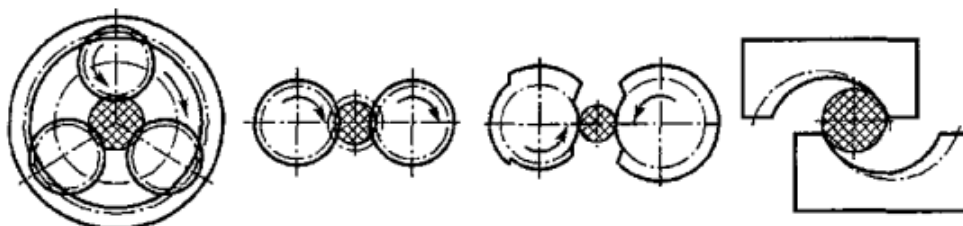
Обробка зубів циліндричними накатниками
